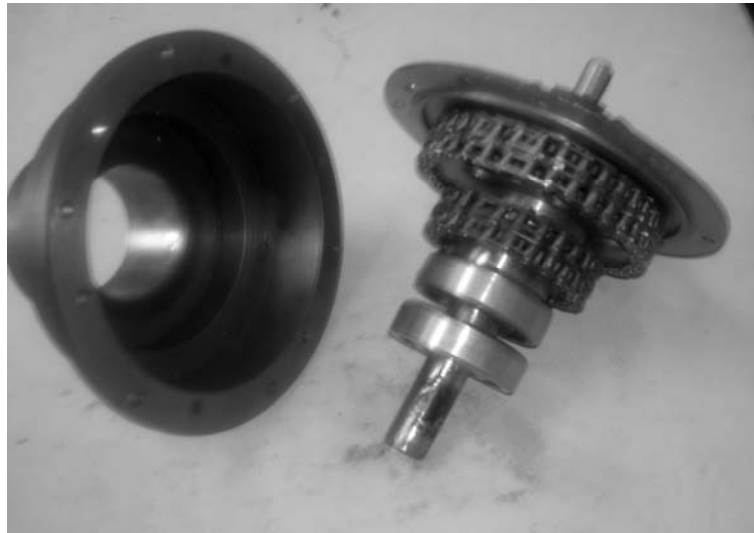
Фотография силового узла передаточного механизма опытного образца цепного планетарного редуктора с передаточным отношением 65
